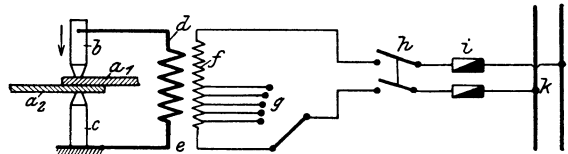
Schaltung und Stromzuführung bei Punktschweißmaschinen.
